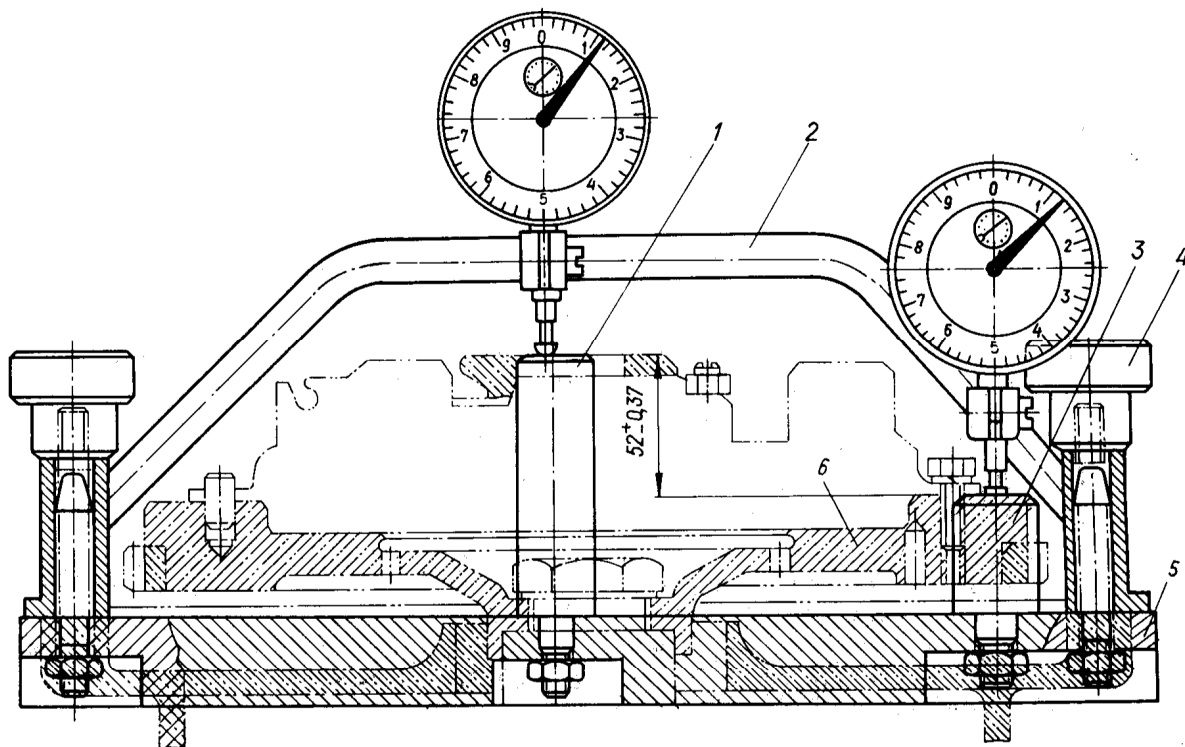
Приспособление для проверки биения торца маховика и для регулировки положения пяты рычагов сцепления:
